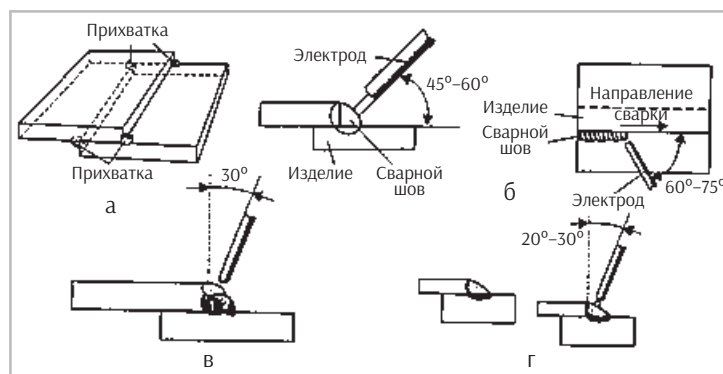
Сварка нахлесточного соединения в нижнем положении: а — подготовка соединения к сварке; б — положение электрода при сварке однопроходным швом равных толщин; в — положение электрода при втором и третьем проходе при выполнении многопроходного шва; г — положение электрода при сварке разных толщин
